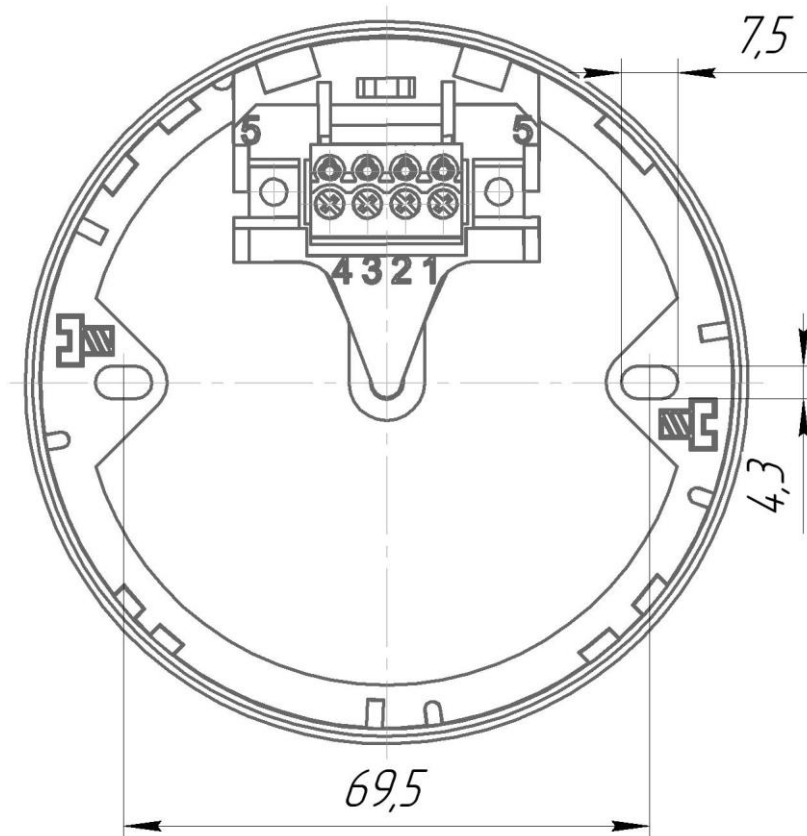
Общий вид звукового пожарного оповещателя без розетки
